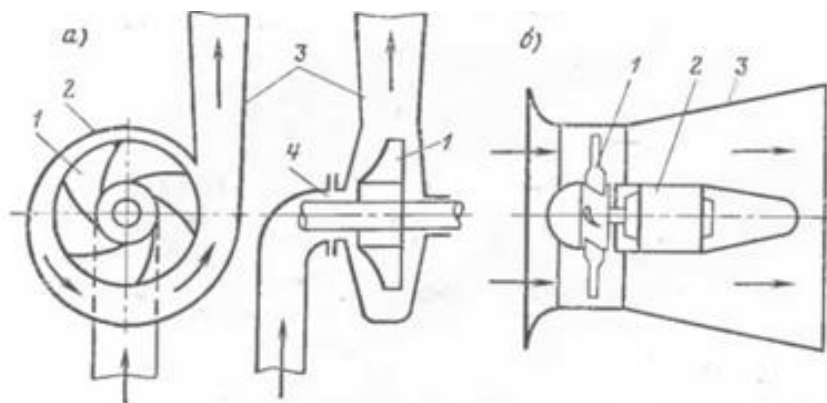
Конструкции центробежного (а) и осевого (б) вентиляторов
